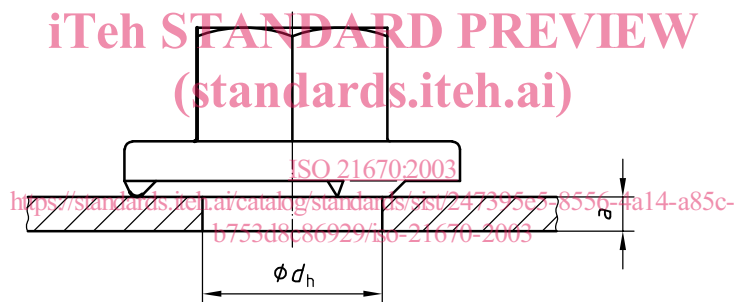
Dimensions associées (écrou non soudé au-dessus)
